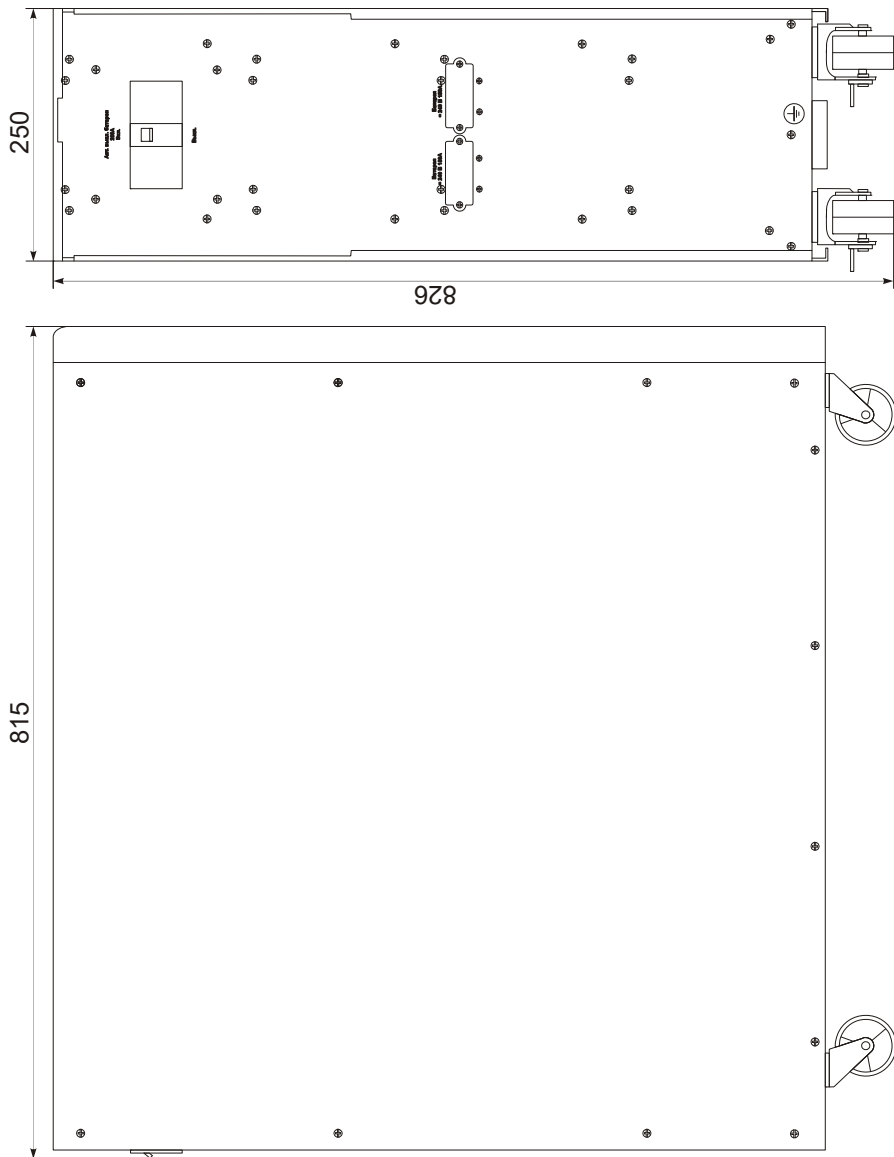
Габаритные и установочные размеры БМ BP 240-36-150A
